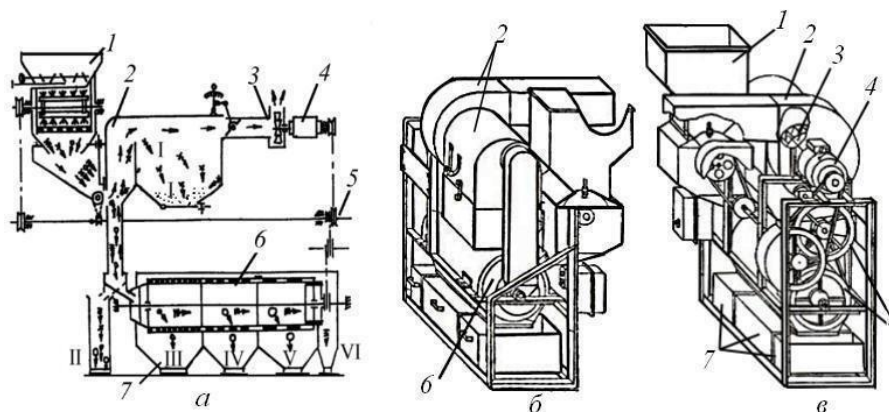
Машина МОС-2: *а* – схема работы; *б* – вид спереди; *в* – вид сзади; 1 – обескрыливатель; 2 – осадочная камера; 3 – вентилятор; 4 – электродвигатель; 5 – вал со шкивами клиноременных передач; 6 – решетный барабан; 7 – ящики;
